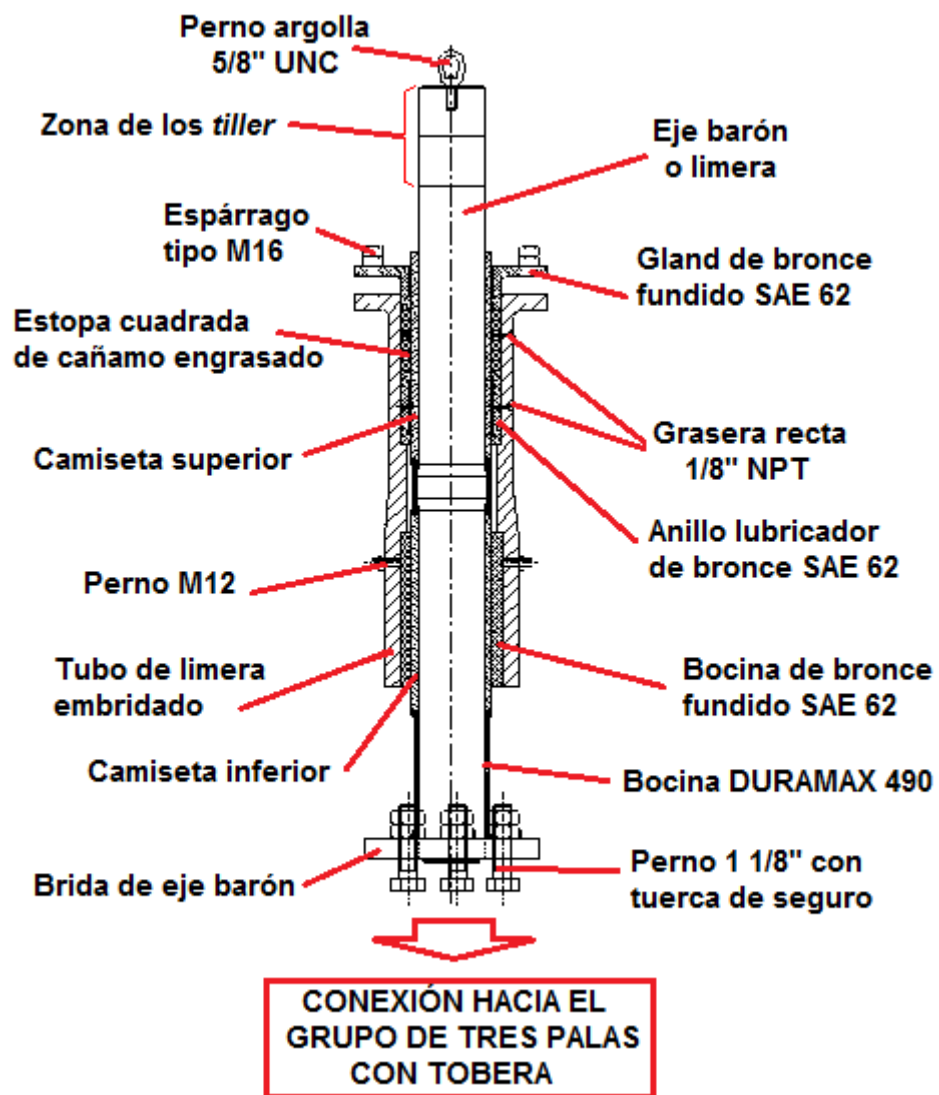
Esquema de los componentes mecánicos del gobierno del remolcador.
